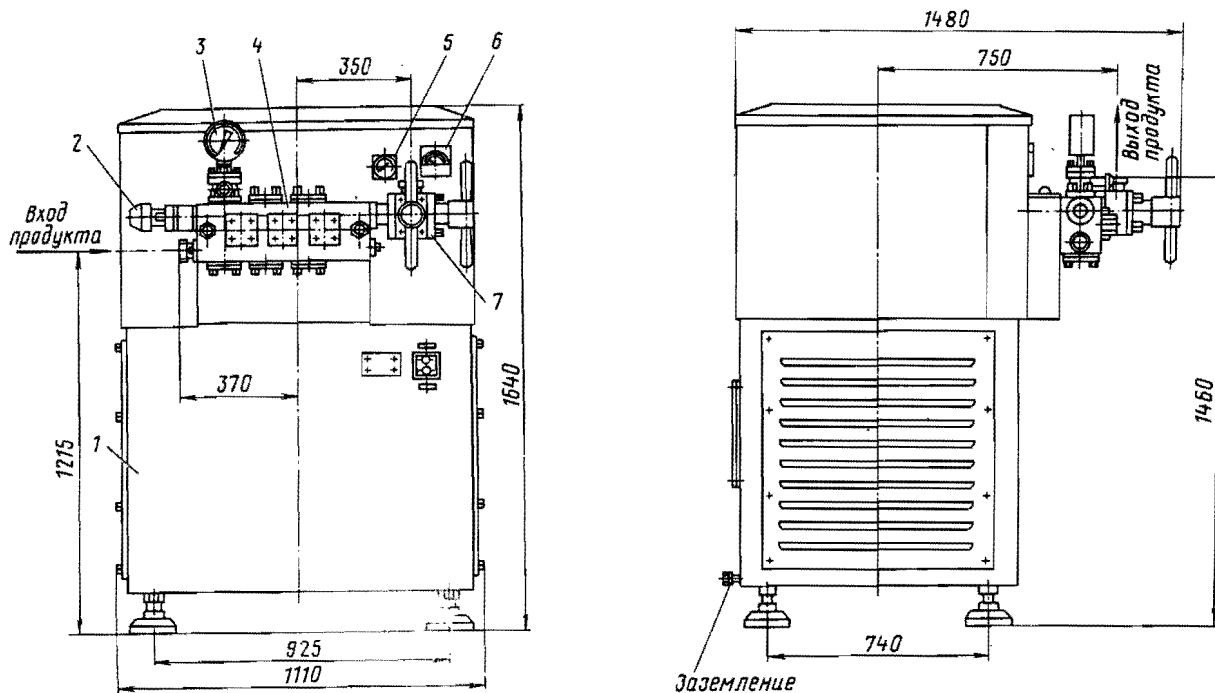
Габаритный чертеж гомогенизатора марки А1-ОГМ:
